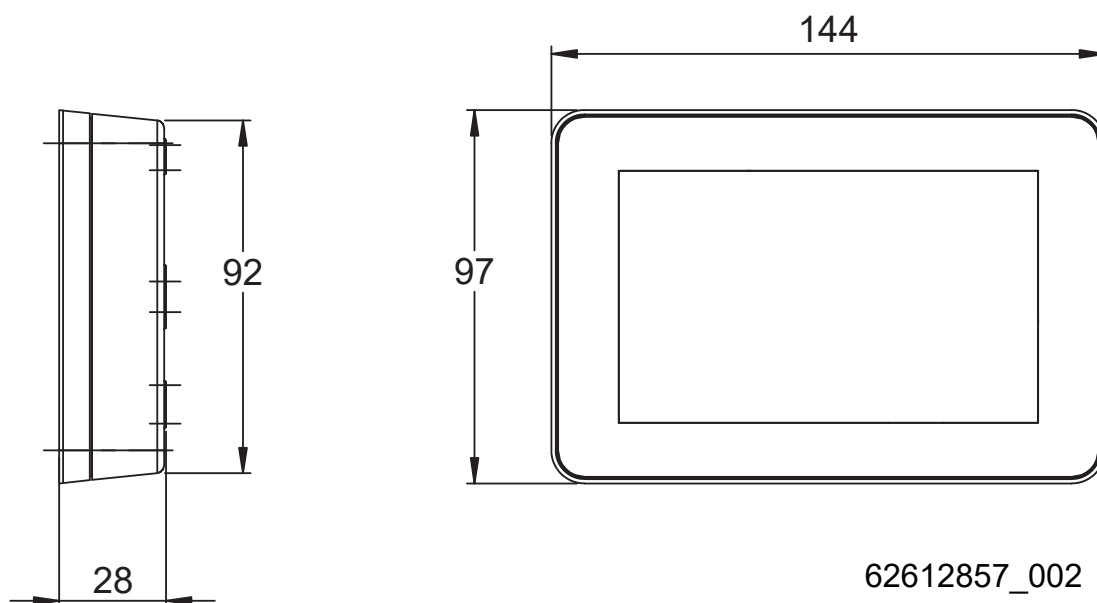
Dimensioni in mm cronotermostato remoto COMODO
